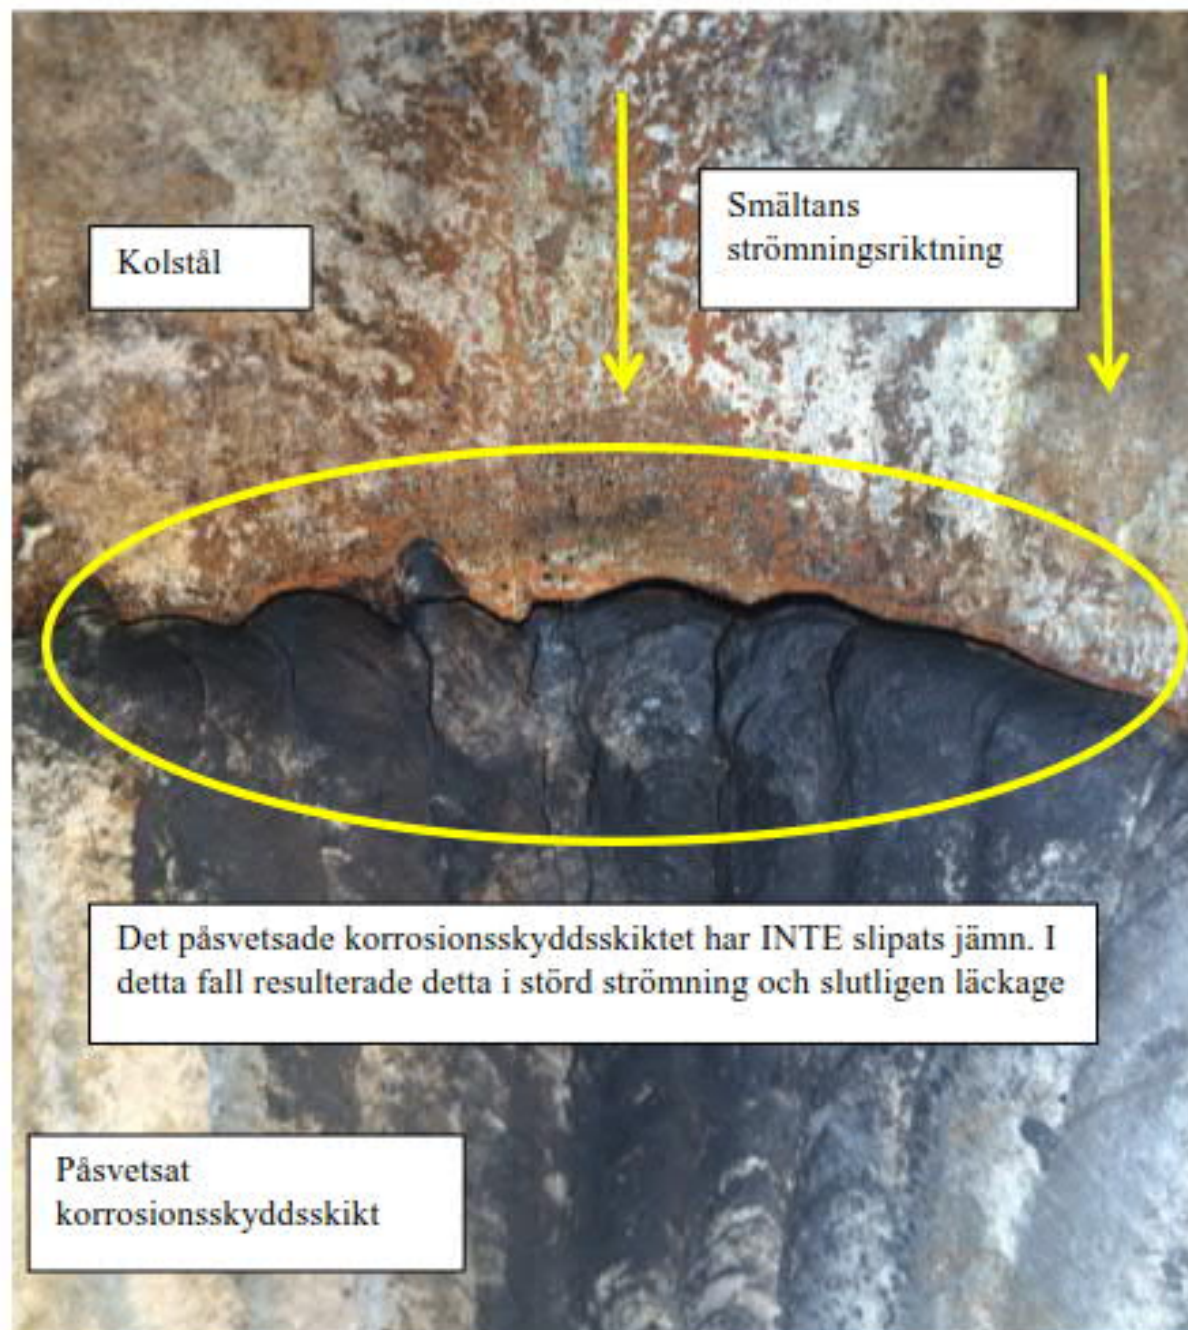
Vid påsvetsningen gäller att desto smalare/tunnare strängar desto bättre.
